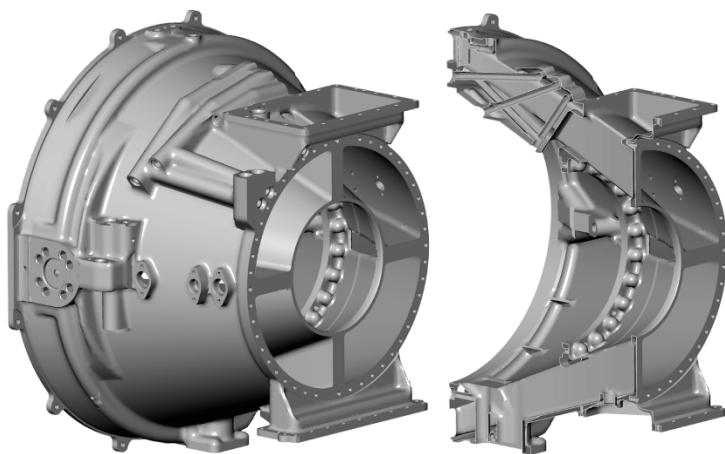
Общий вид и сечение разработанной CAD-модели входного корпуса
